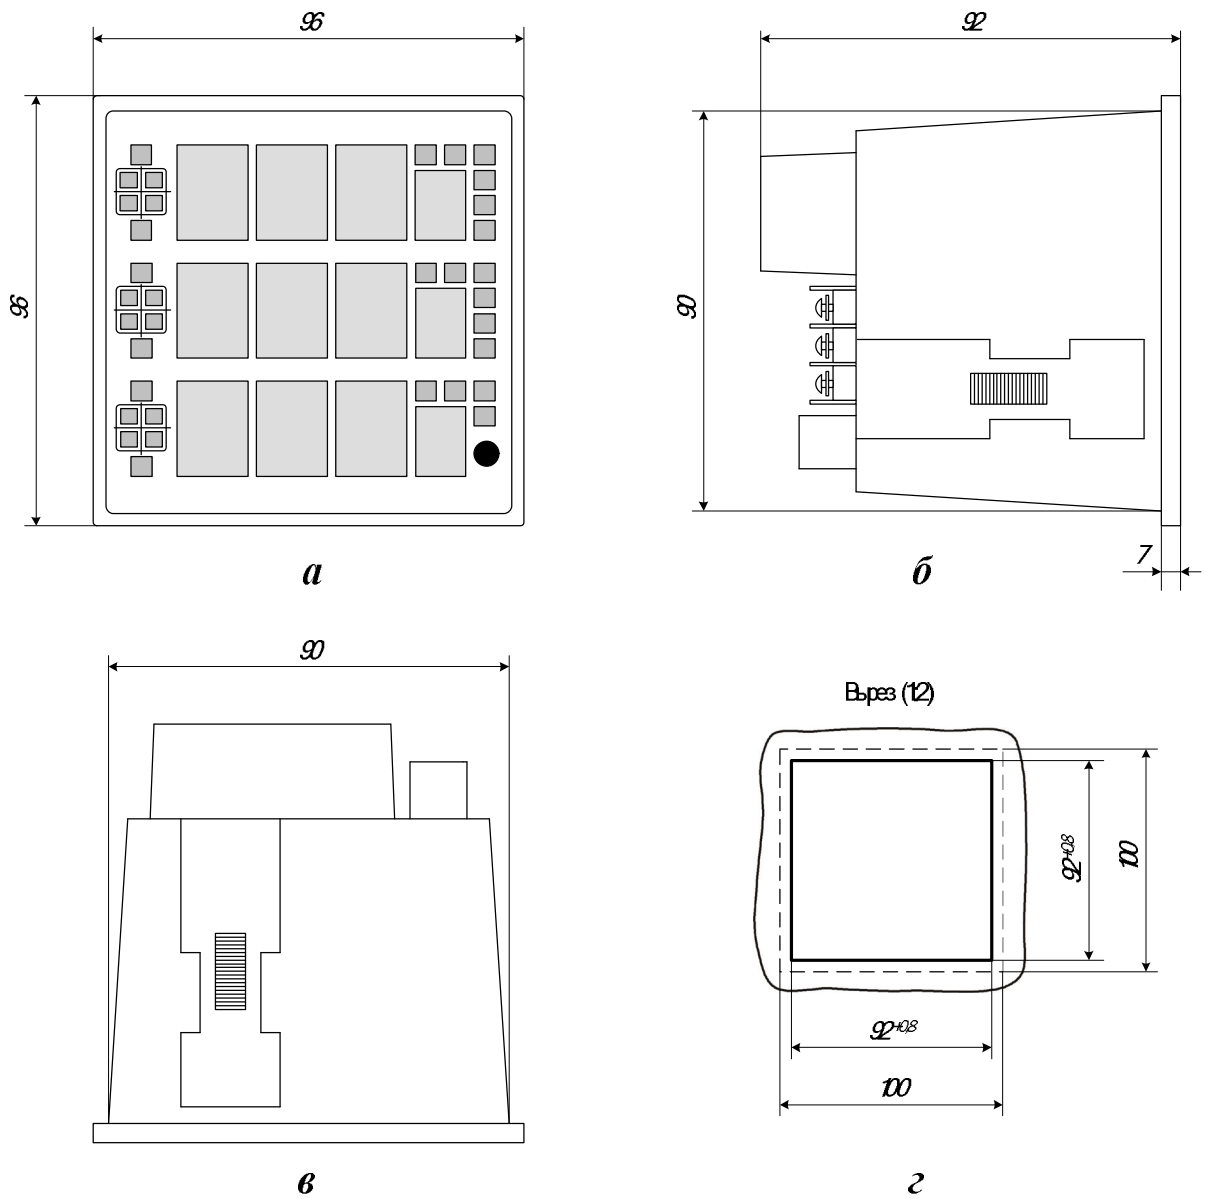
Общий вид, габаритные и установочные размеры прибора ЩМК96:
